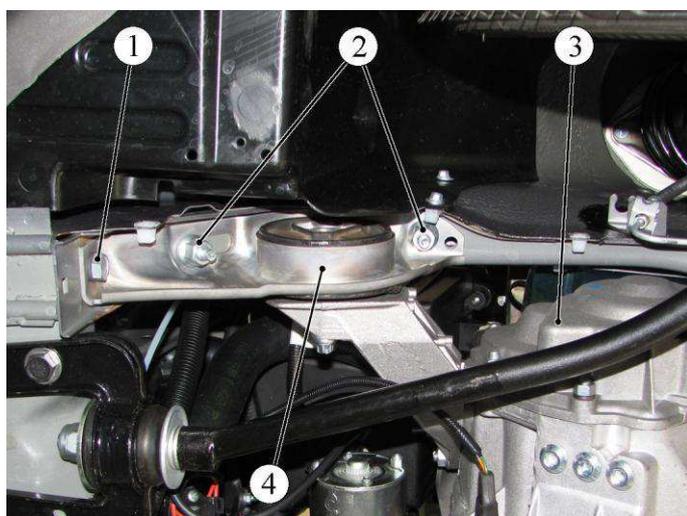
Отсоединение левой опоры подвески двигателя:
